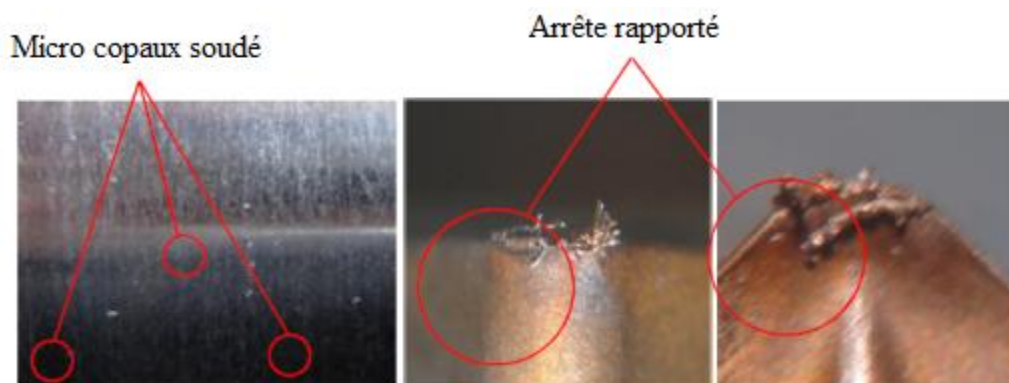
Micro-copeaux soudé sur la surface usinée et arête rapportée sur plaquette de coupe.
